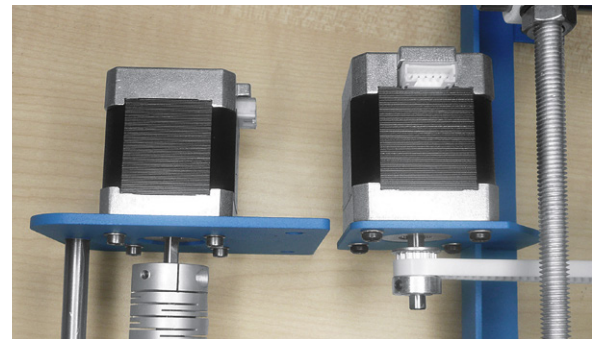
Hier sieht man den Grund, warum die Schrauben für den Y-Motor (rechts) zu lang sind: Das Montageblech ist dünner als z. B. die Z-Motor-Aufnahmen (links).
